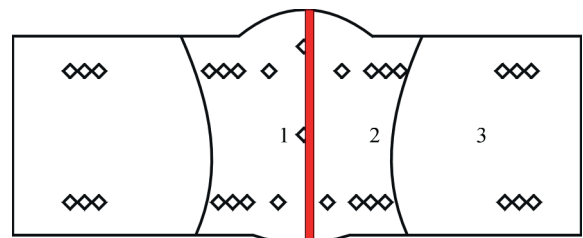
Результати випробувань зварного зразка на твердість за Віккерсом: 1 – зварний шов; 2 – ЗТВ; 3 – основний метал
